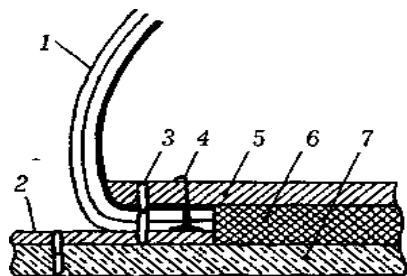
Рантовый метод крепления подошвы: 1 – заготовка; 2 – основная стелька с губой; 3 – простилка; 4 – губа стельки; 5 – основной рант; 6 – подошва; 7 – внутренний и наружный швы
